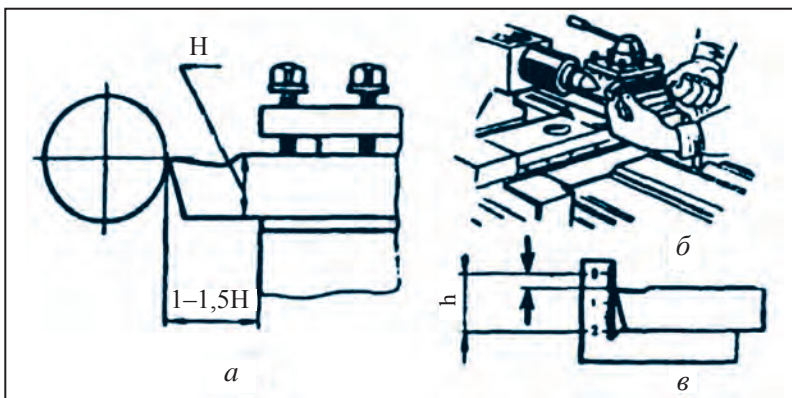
Установка резца: а) резец в резцедержателе; б) проверка высоты резца; в) угольный шаблон.
